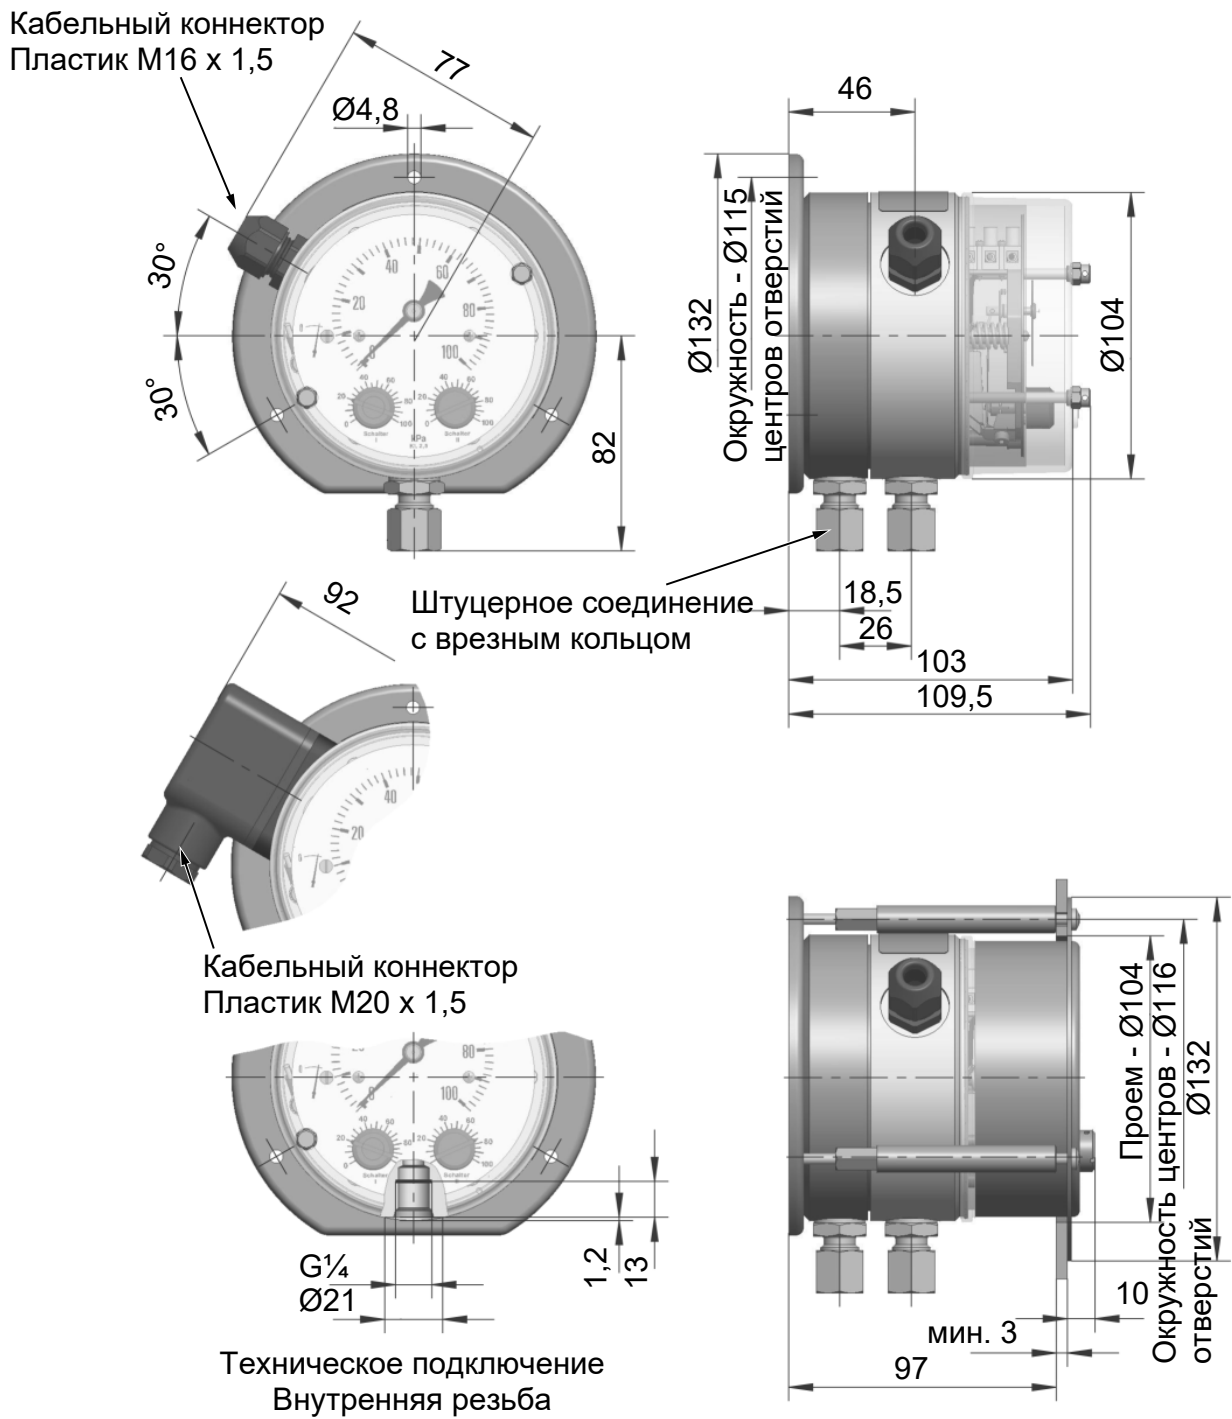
Напорная камера из нержавеющей стали (IP55)
